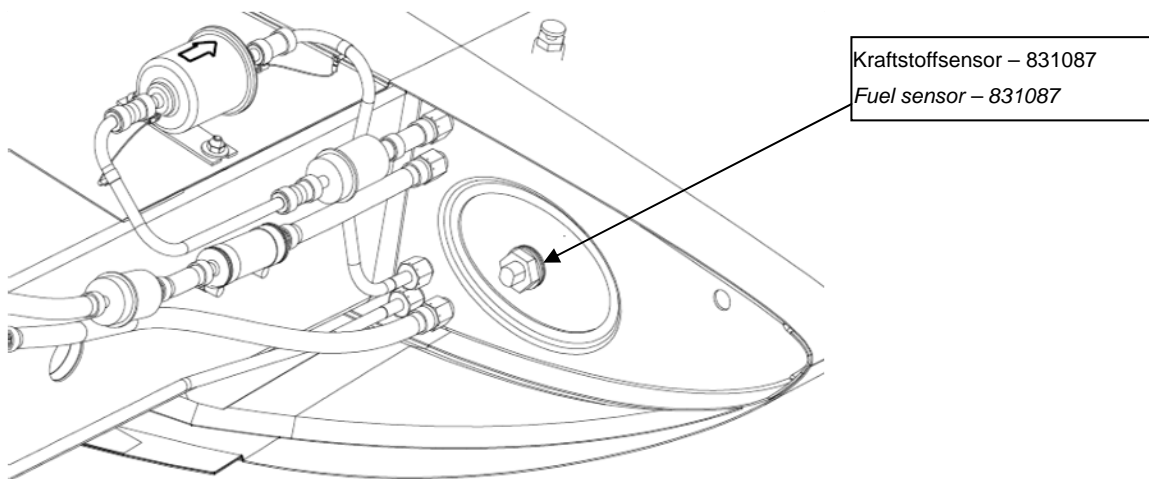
Ausschnitt von Ansicht Unterseite Innenflügel rechts
